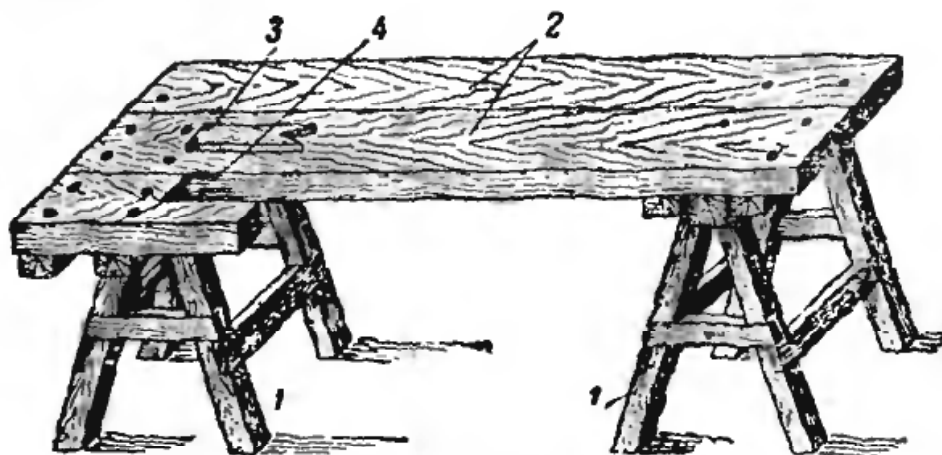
Упрощённый верстак: 1 — козлы; 2 — верстачная доска; 3 — упорный брусок с клиновидным вырезом; 4 — вырез для зажима клином.
